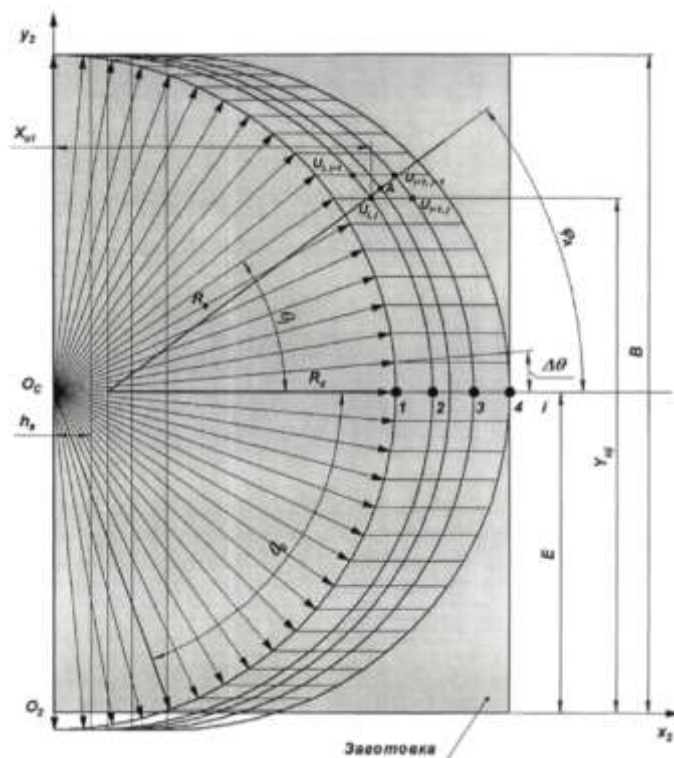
Схема розташування вузлів полігональної сітки, що покриває оброблювану поверхню заготовки
